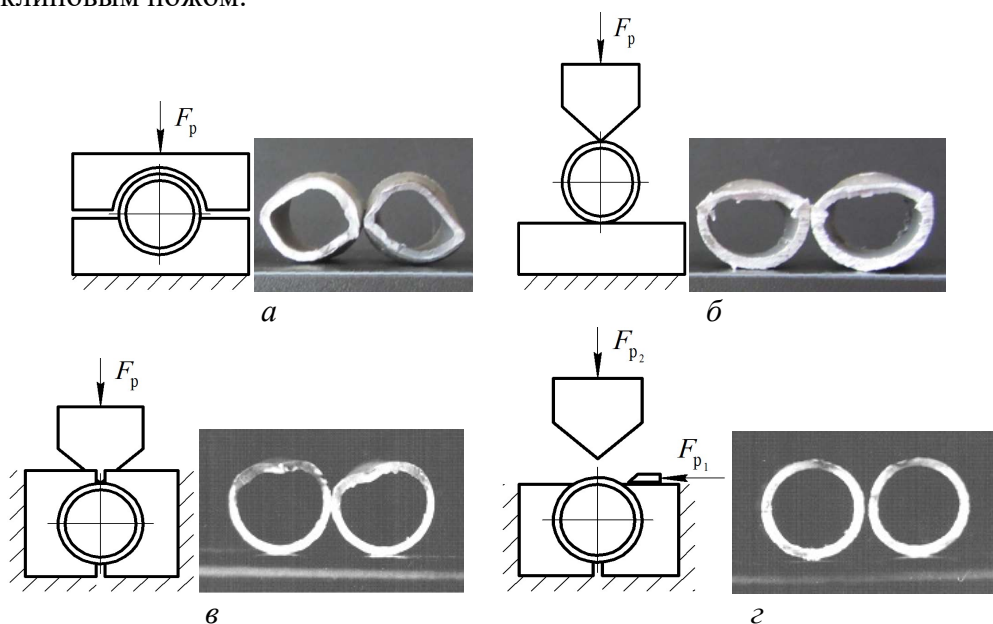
Существующие способы поперечной резки тонкостенных труб ножами и обеспечиваемое ими качество торцевых поверхностей полых профилей
